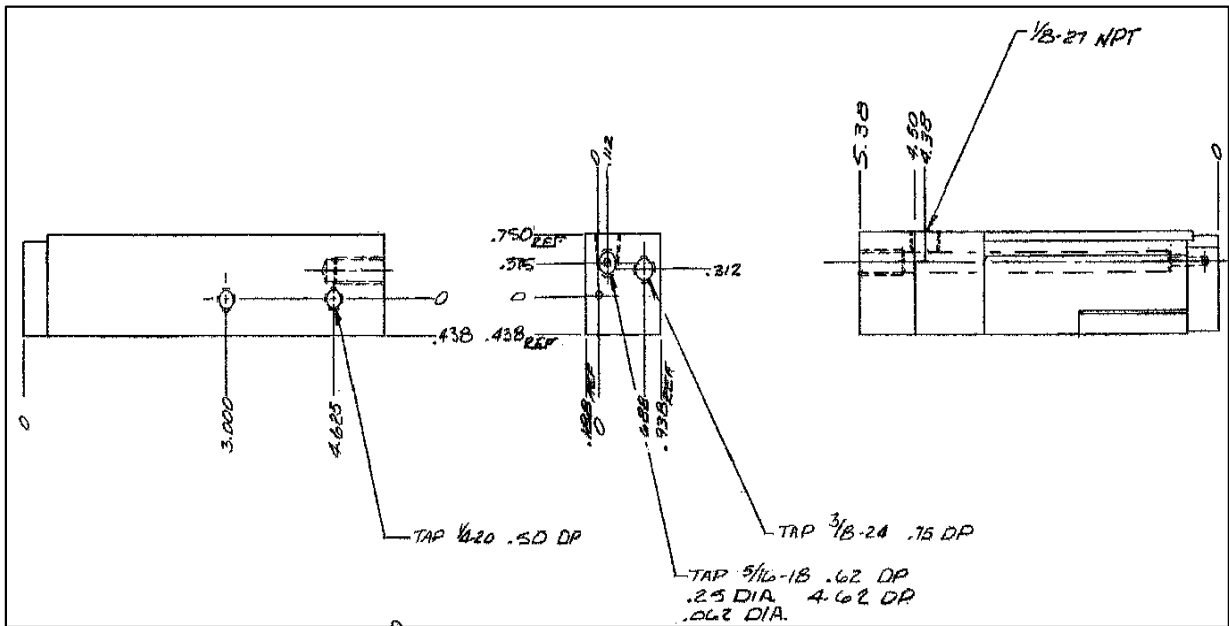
Sección del plano donde es especificado el cargador de terminal máquina CA-3786, Fuente (Schneider Electric 2020).
